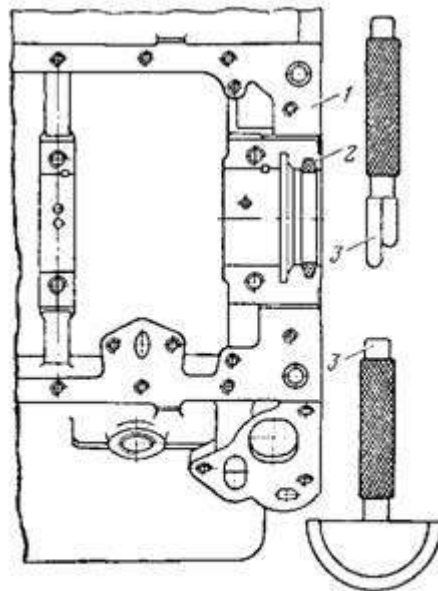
Оправка для уплотнения заднего коренного подшипника двигателя ЗИЛ-130:
